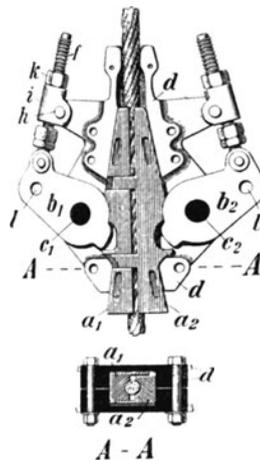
Seilklemme der Deutschen Maschinenfabrik A-G.
